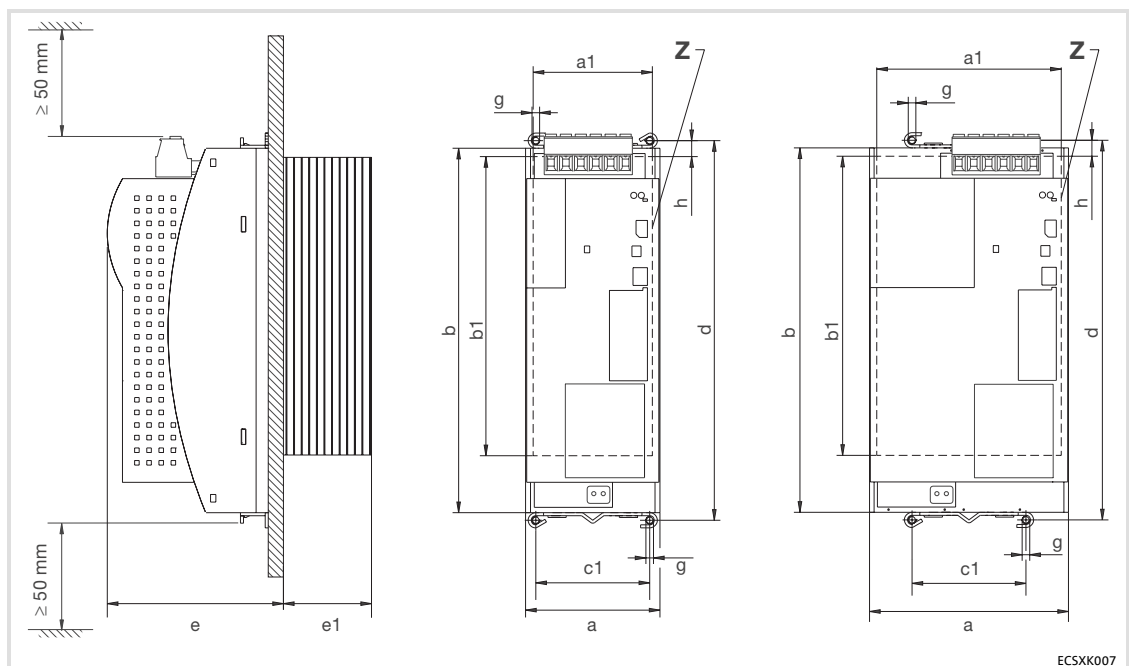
Abmessungen bei Montage thermisch separiert, Typ ECSDKxxx
